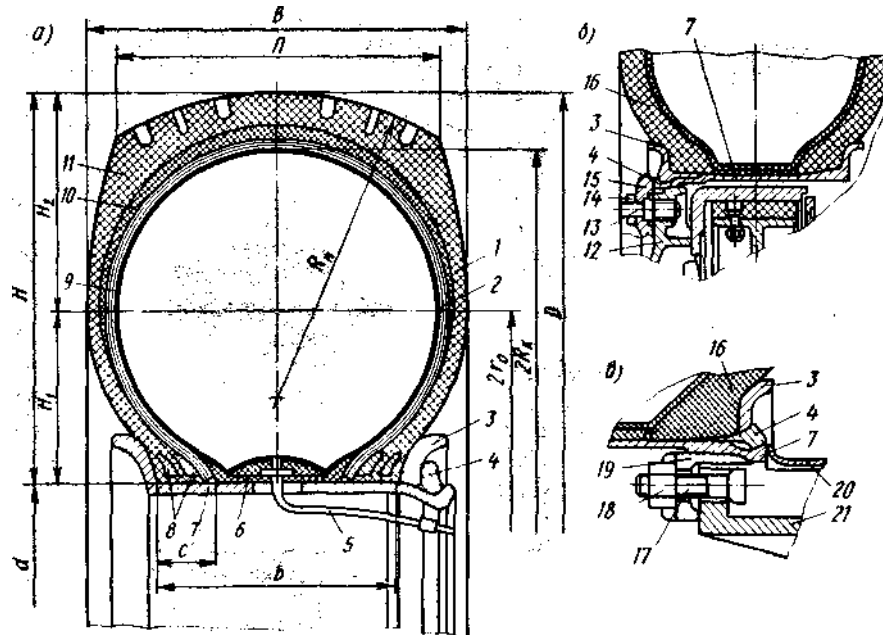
Конструктивні елементи бездискового пневматичного колеса тролейбусів ЗиУ–9: а – пневматична шина; б – кріплення одиночного (керованого) колеса; в – кріплення здвоєного (ведучого) колеса
